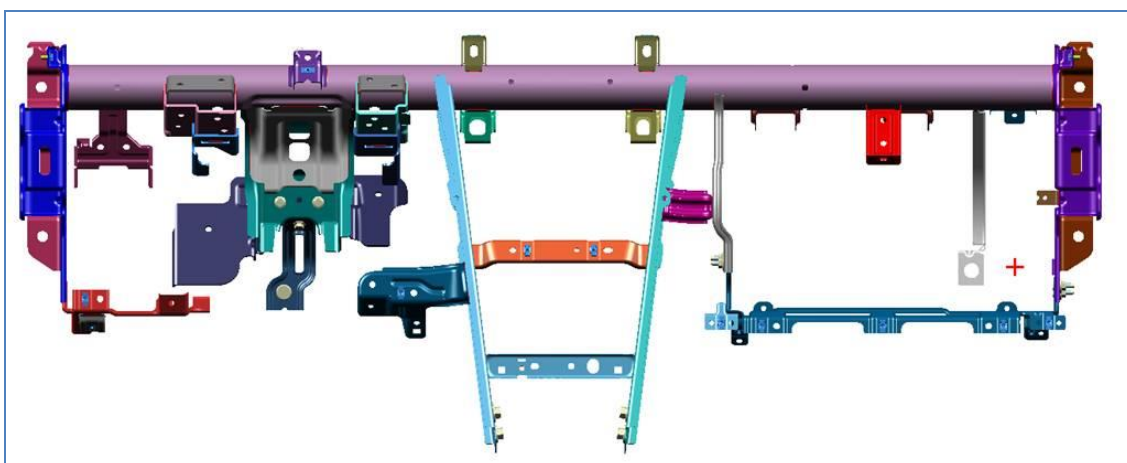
Cockpit, cross car beam, soporte salpicadero
